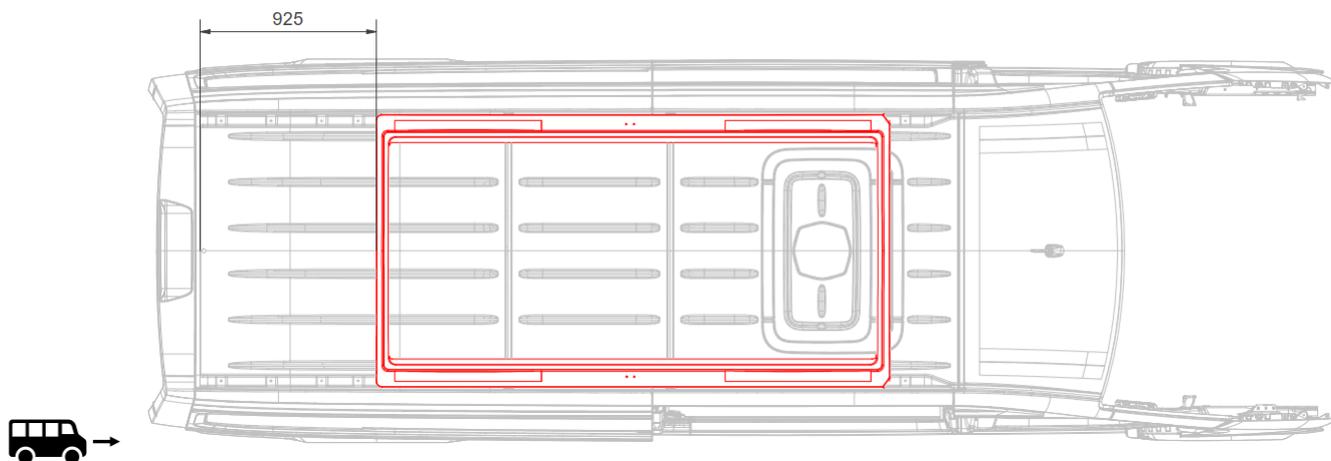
VW Crafter L4H3 (L = 6836 mm) [G0002143-001]
